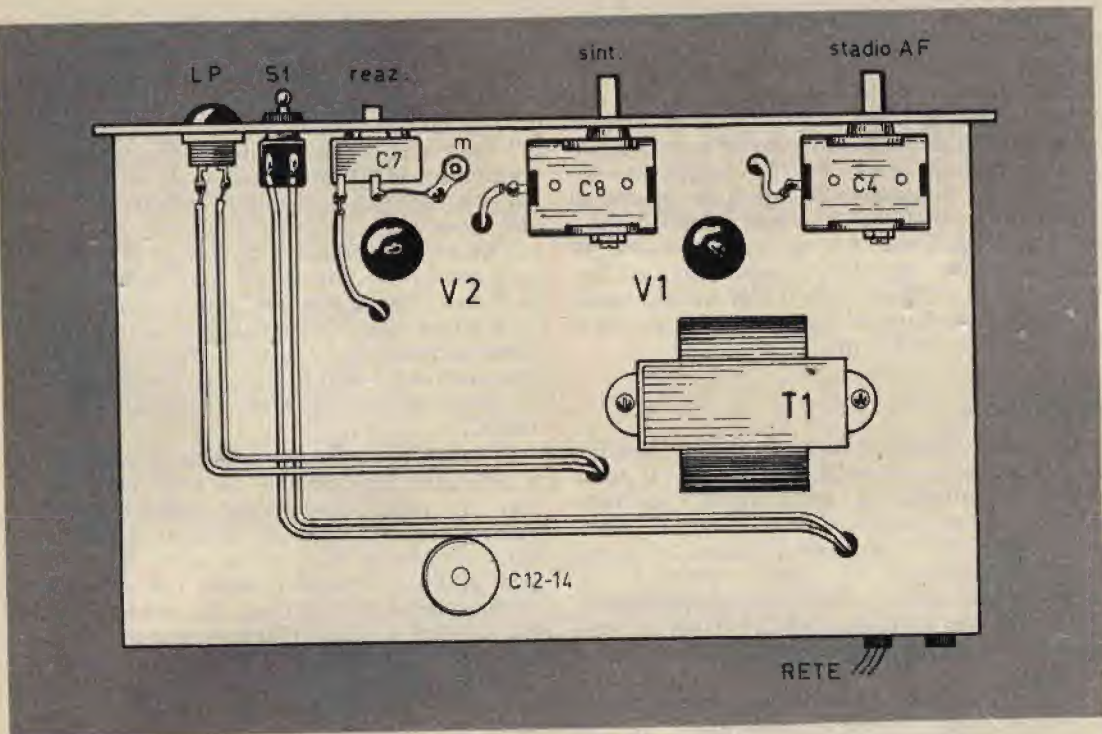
Montaggio dei componenti nella parte di sopra del telaio e sul pannello frontale.
